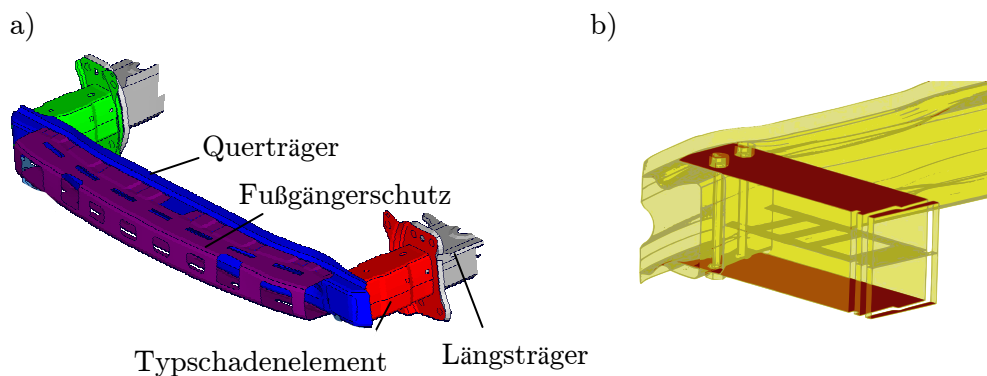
Vorderwagenstrukturen: a) Stahlblechkonstruktion, b) Aluminiumprofil
